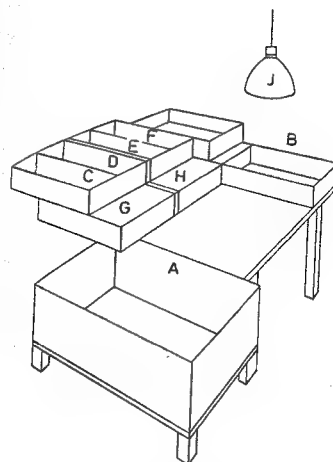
Disposición del lugar de trabajo para la inspección de carretes metálicos. Método antiguo: A, carretes que han de ser inspeccionados; B, carretes buenos; C-D-E-F-G-H, carretes rechazados. La luz procede de la lámpara J.
